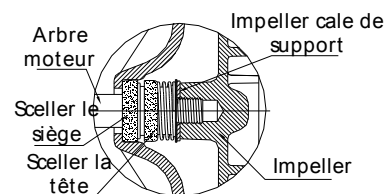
A-Le cachet mécanique qui remplace 5PXE2A a 5PXE7A
